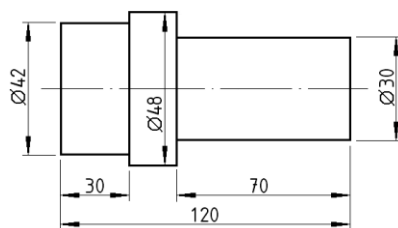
Vista do corpo de prova pré-usinado (cotas em mm)
